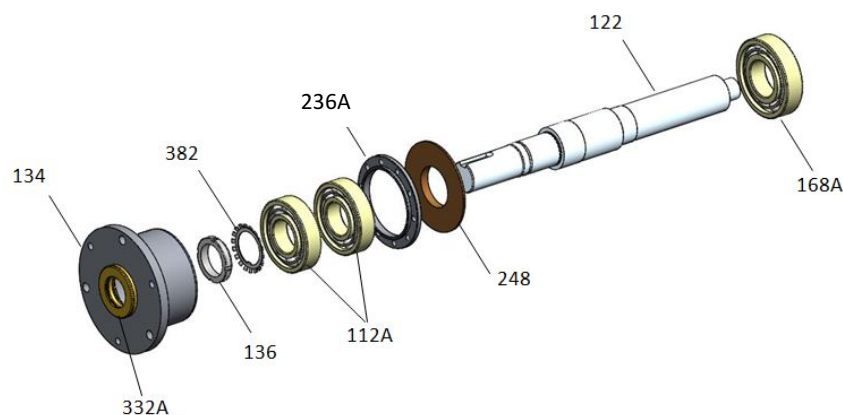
Extracción del rodamiento - Grupo 1 y 2 de rodamientos dobles
